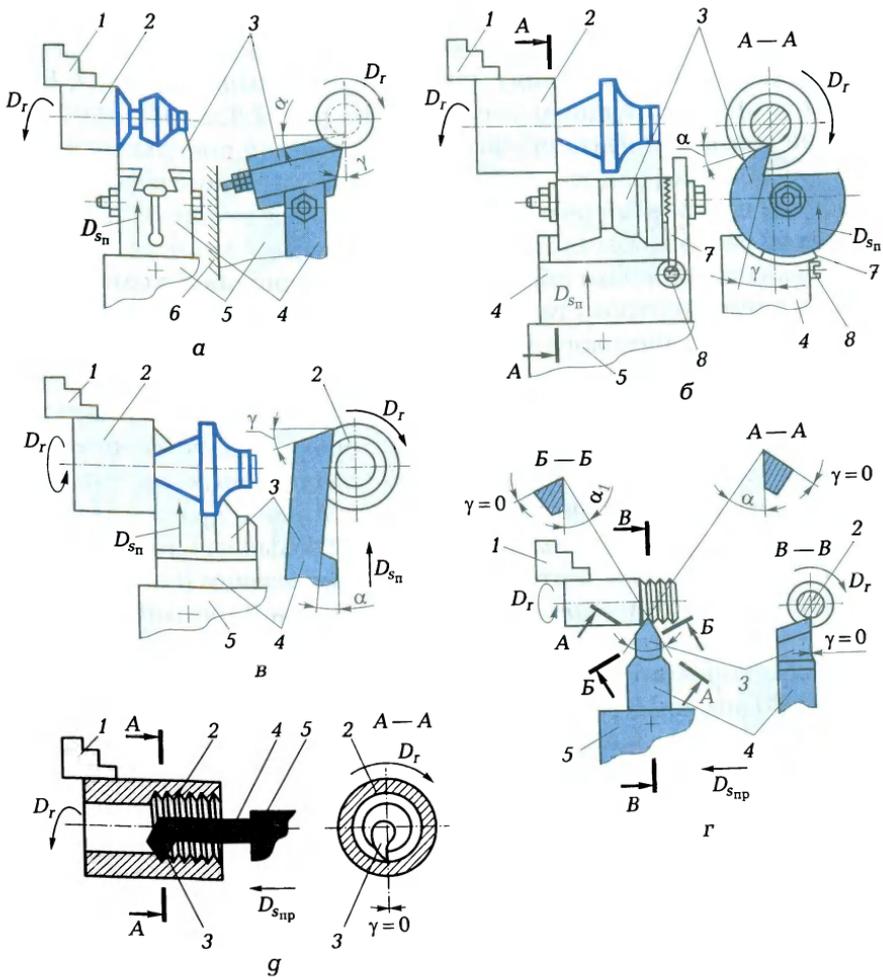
Схемы точения фасонных поверхностей и резьб на токарно-винторезном станке:
